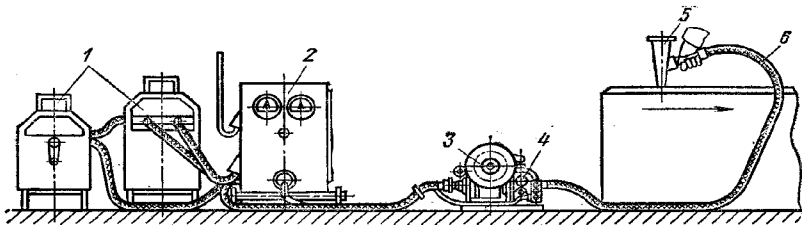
Шланговий напівавтомат для зварювання під шаром флюсу
